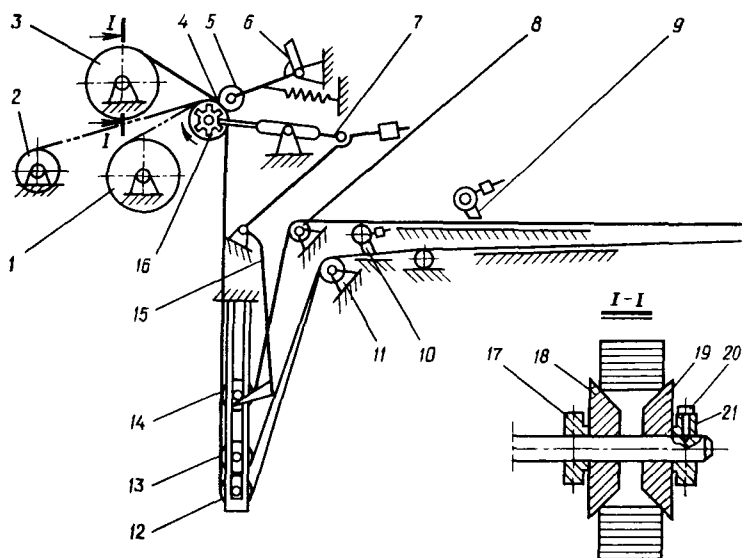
Кинематическая схема питателя машин типа КЗП-1 для рулонного упаковочного материала с разматывающим роликом и компенсатором
